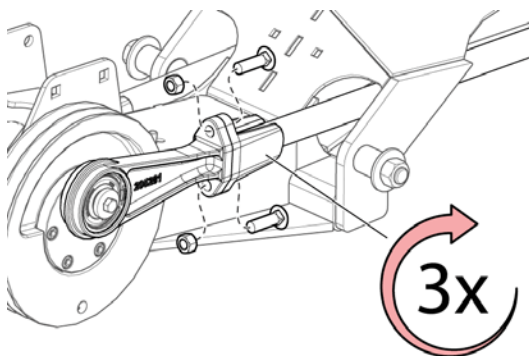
Затяните правый рычаг привода ножа на 3 оборота
